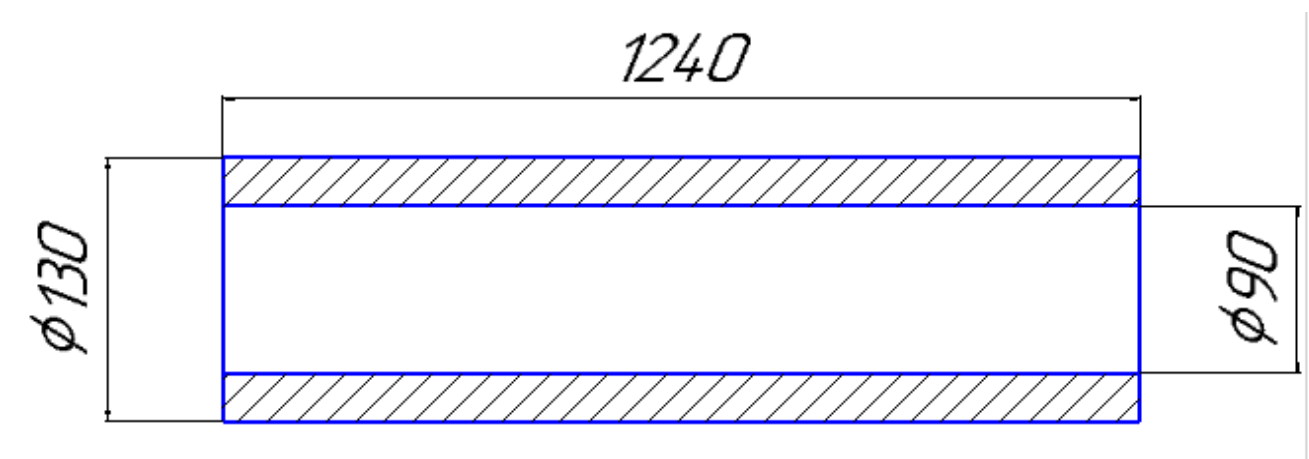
Заготовка корпусу ЧП-63
